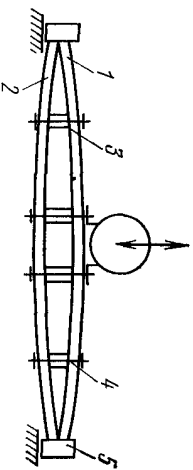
Схема установки для сборки пакета деталей рамной конструкции
